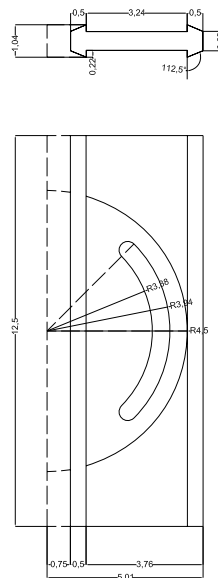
Diseño de perfil para extrusión (planta) y de figura para troquel ( alzado) en placa de contraventeo:
